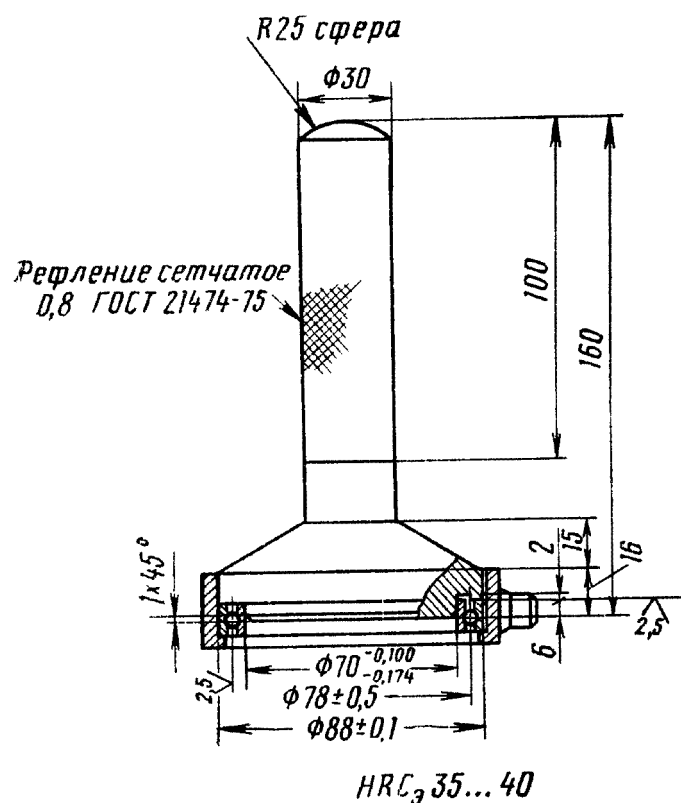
Оправка для установки подшипника в обойму механизма блокировки дифференциала заднего моста
